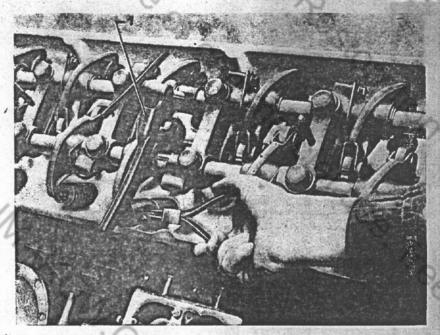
Auswechseln einer Ventilfeder 1 Sonderwerkzeug
